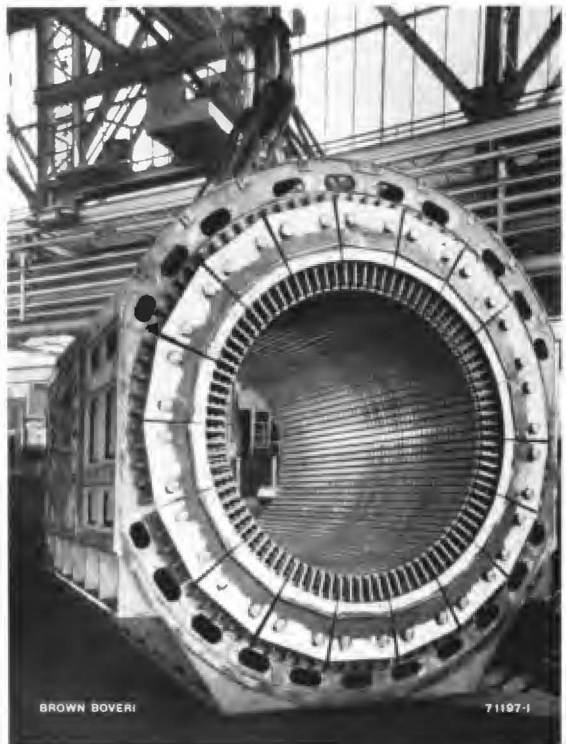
Geblechter Stator einer Synchronmaschine für 22 kV Spannung
